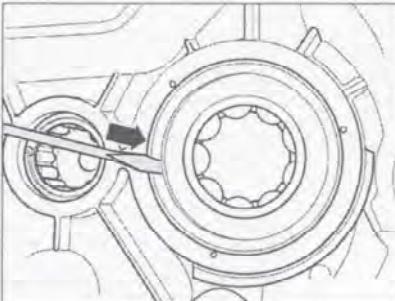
Извлечение переднего подшипника первичного вала.
